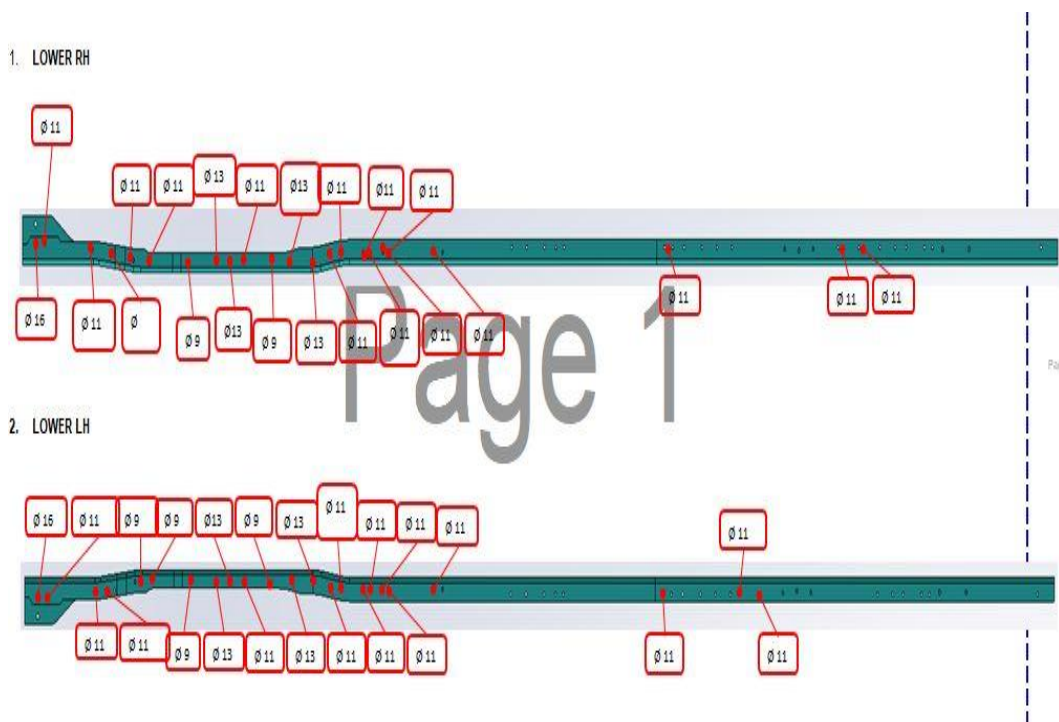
Drawing hole* Lower RH dan LH tipe HD
